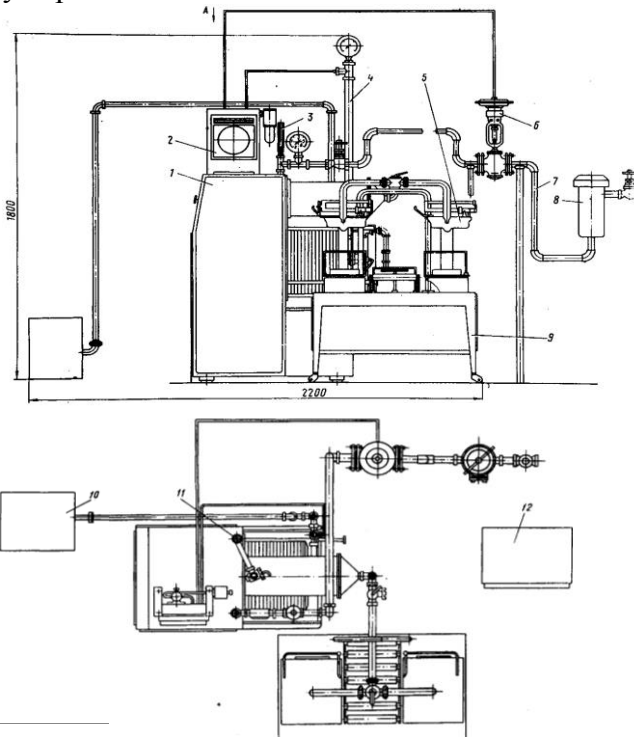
Загальний вигляд установки-марки РЗ-ОУА:
